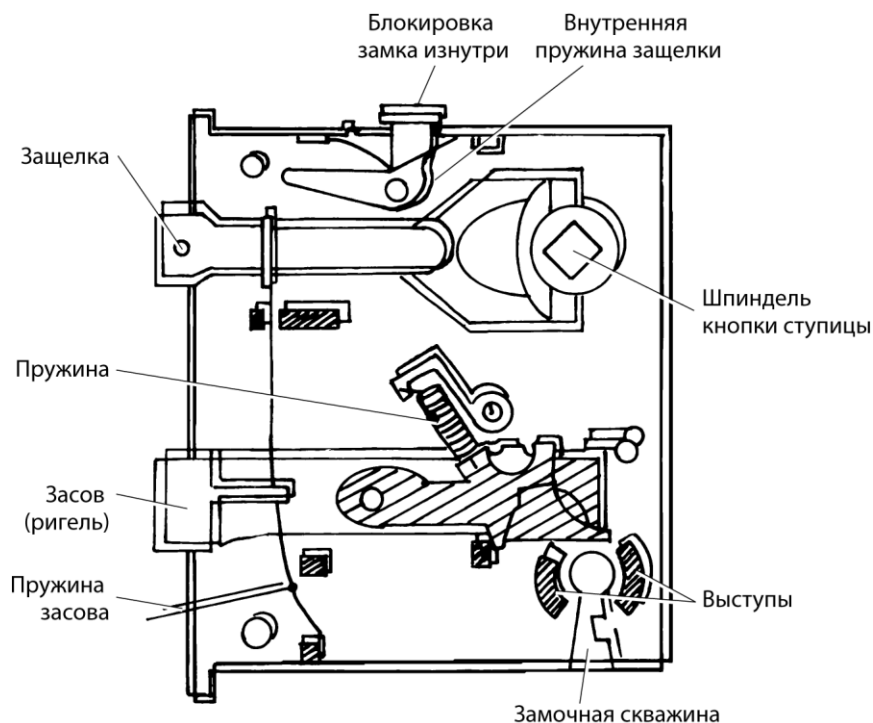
Устройство типичного накладного замка под ключ с бородкой
